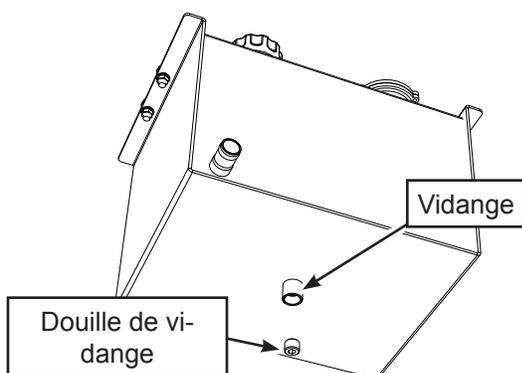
RÉSERVOIR : VUE DU DESSOUS
